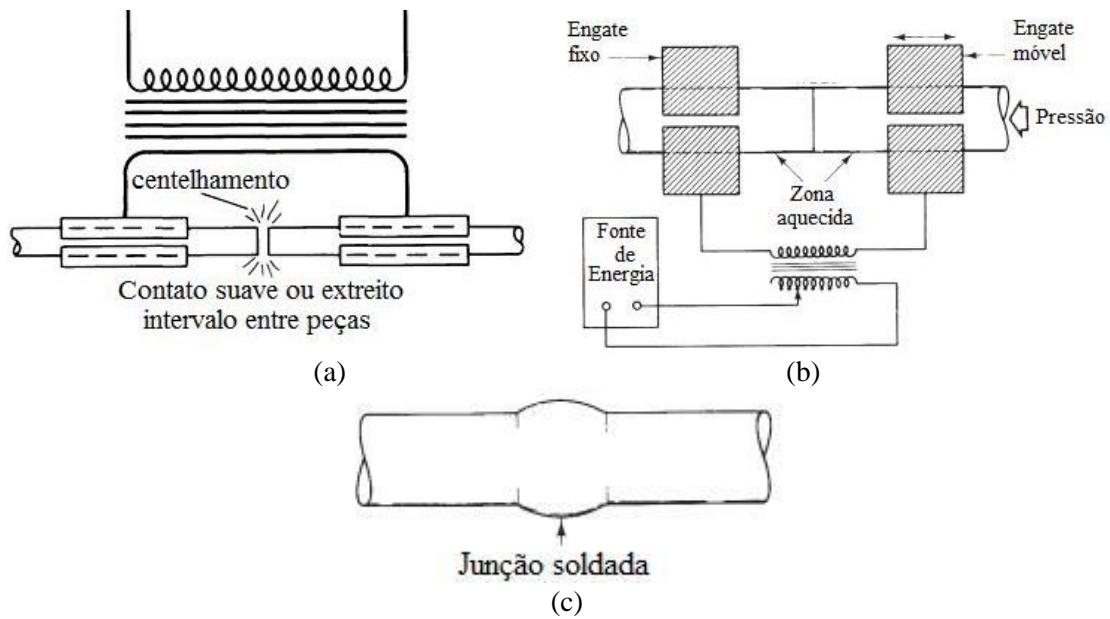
Princípios do processo de soldagem elétrica por centelhamento (*Flash Butt Welding*). Estágio de centelhamento (a), estágio de forjamento (b) e junta soldada acabada (c). Fonte: Samardžić *et al.*, 2011; ASM HANDBOOK VOL. 6, 1993.
